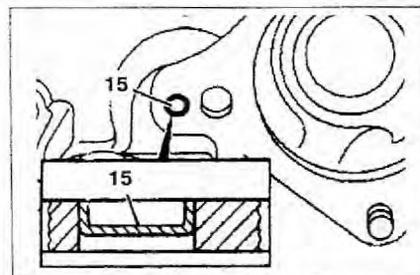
Используя пробойник, извлеките крышку 15 из корпуса коробки передач.
